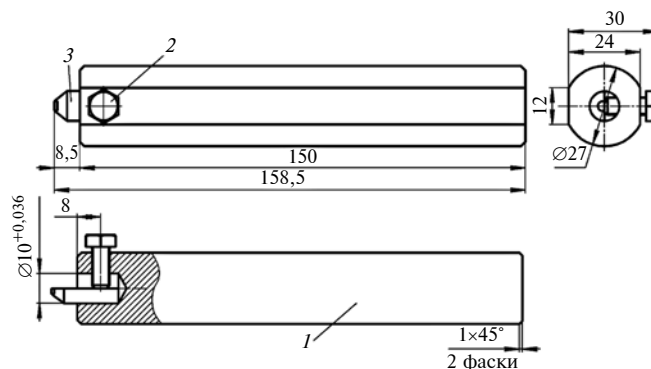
Спроектированный специальный инструмент для упрочнения поверхностного слоя:
